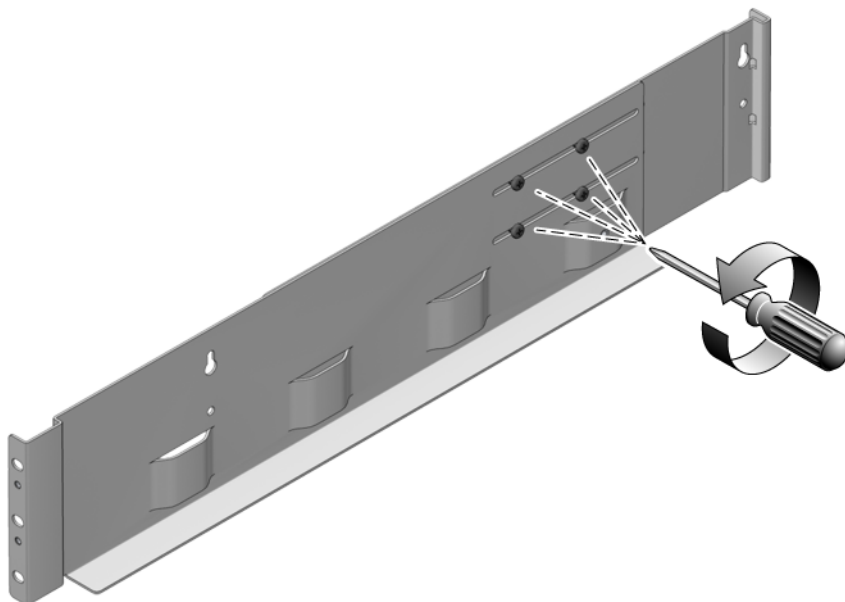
Desserrage des vis des rails pour régler la longueur des rails du plateau d'extension
